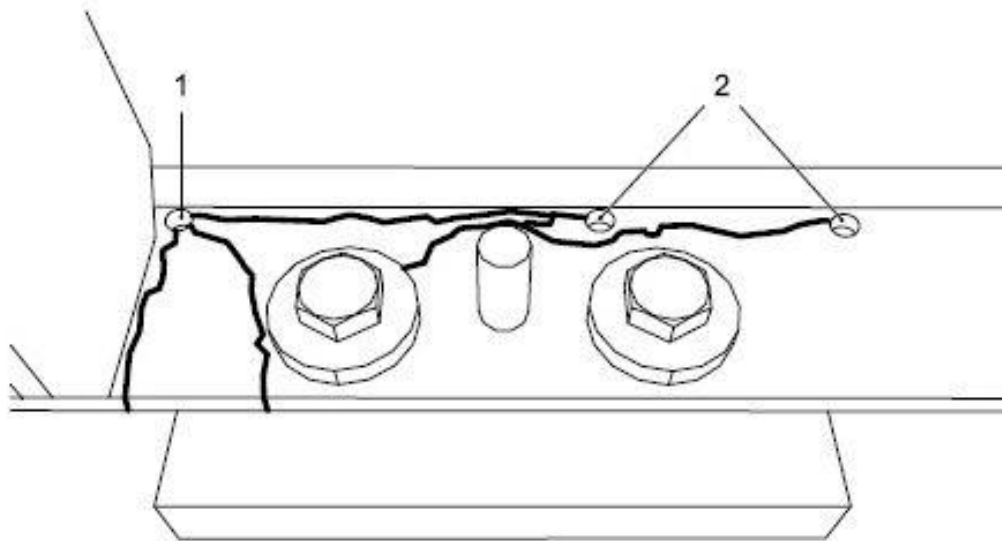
Taladrado de finales de fisuras (paso 2).
